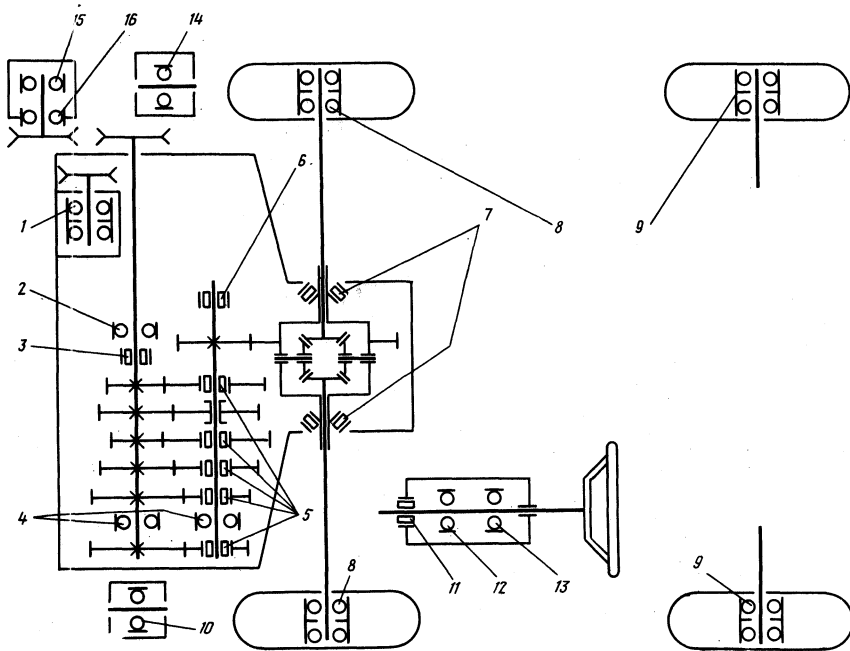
Схема расположения подшипников качения на автомобиле ВАЗ-2108: 1 — шариковый радиальный двухрядный 6-330802ЕС17; 2 — шариковый радиальный 360106КС23; 3 — роликовый радиальный 66-42205АЕ; 4 — шариковый радиальный 6-50305А1Е; 5 — роликовый радиальный игольчатый 464706Е1; 6 — роликовый радиальный 66-42305АЕ; 7 — роликовый конический 6У-7207А; 8 — шариковый радиально-упорный двухрядный 6-256907Е1С17; 9 — шариковый радиально-упорный двухрядный 6-256706Е1С17; 10 — шариковый упорно-радиальный 348702С23; 11 — роликовый игольчатый 604901ЕУС17; 12 — шариковый радиальный 80-903е; 13 — шариковый радиальный 1000805; 14 — шариковый радиальный 7690906; 15 — шариковый радиальный 6-1802С1У1С9; 16 — шариковый радиальный 6-180302У1С9
